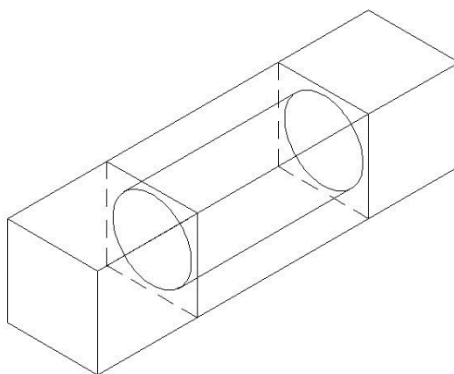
Конструкция комбинированного контейнера с котлом цилиндрической формы
